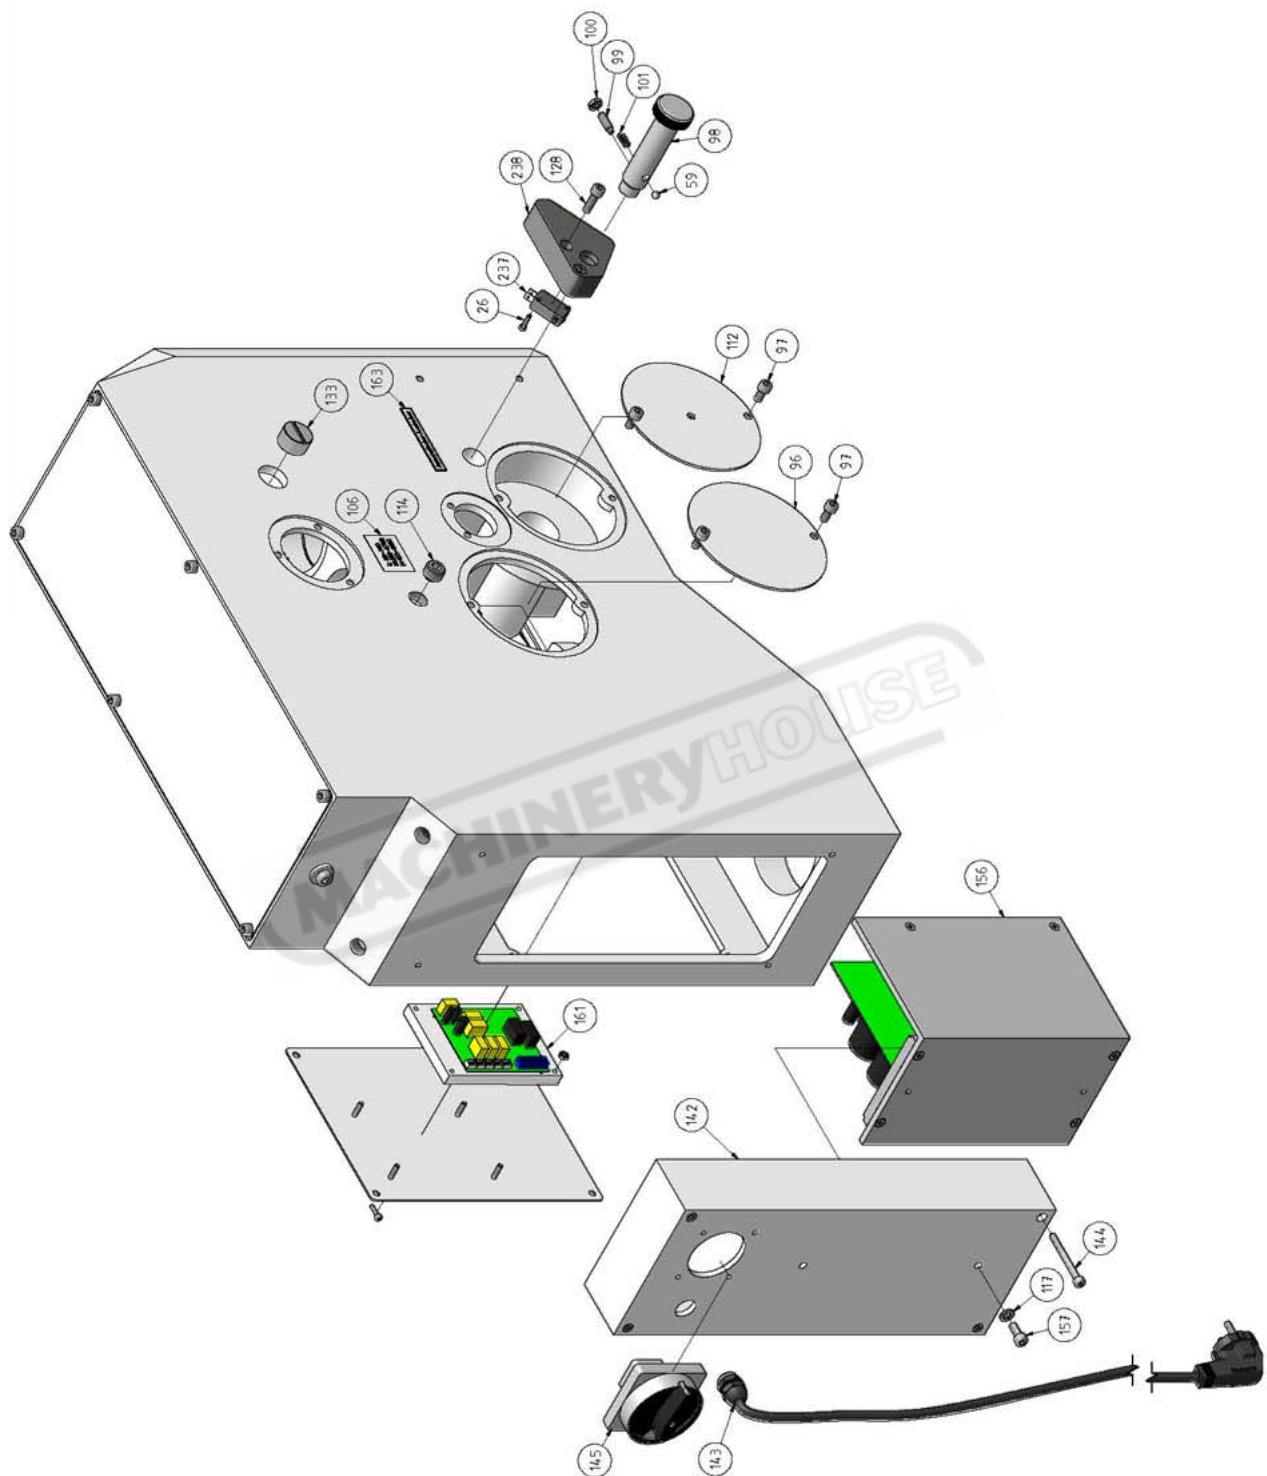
Bohrkopf 9 von 9 - Drilling head 9 of 9
